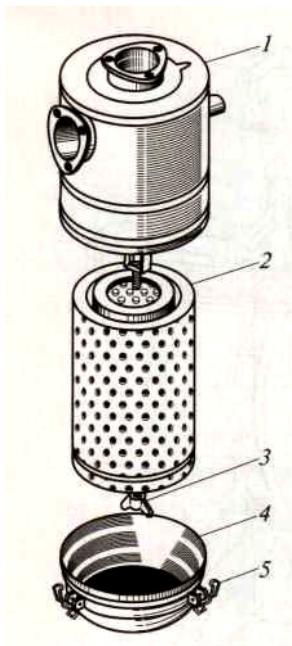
Воздушный фильтр двигателя КамАЗ:
